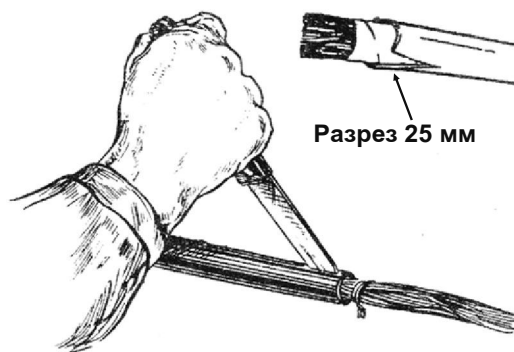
Разрезание оболочки для установки соединителя 4460-D.
